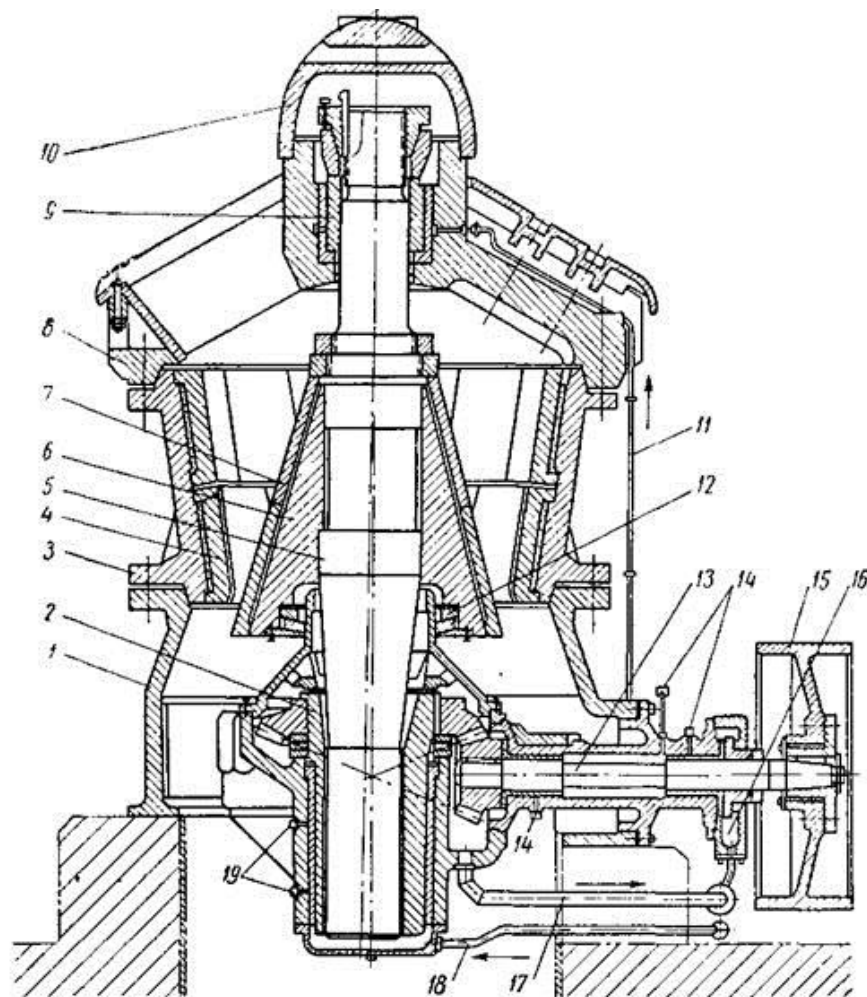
Конусна дробарка: 1- нижня частина станини; 2 - ексцентрик; 3 - середня частина станини; 4 - броня; 5 - вал конуса; 6 - корпус конуса; 7 - броня; 8 - траверса; 9 - обойма верхнього підвісу; 10 - ковпак; 11 - труба для підведення густого змащування; 12 - протипиловий пристрій; 13 - приводний вал; 14 - термодатчики приводного валу; 15 - шків; 16 - маслозбірник; 17 - труба для зливу масла; 18 - маслопідвідна труба; 19 - термодатчики ексцентриккового вузла
